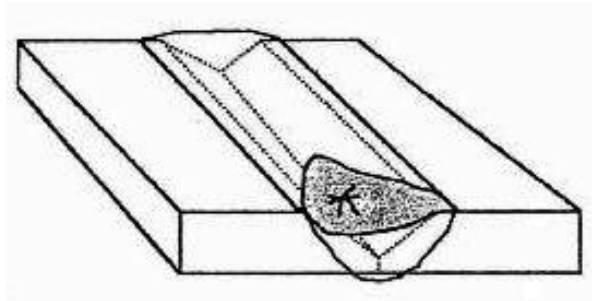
GRIETAS EN EL CRÁTER
